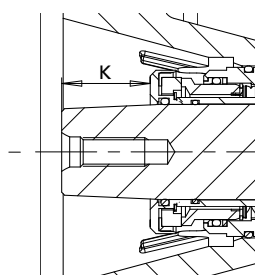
Medida de control "K" del extremo del eje hasta el cierre mecánico de cartucho doble de KSB
